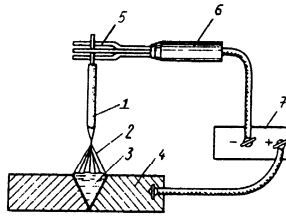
Схема зварювання з електродом, що плавиться
